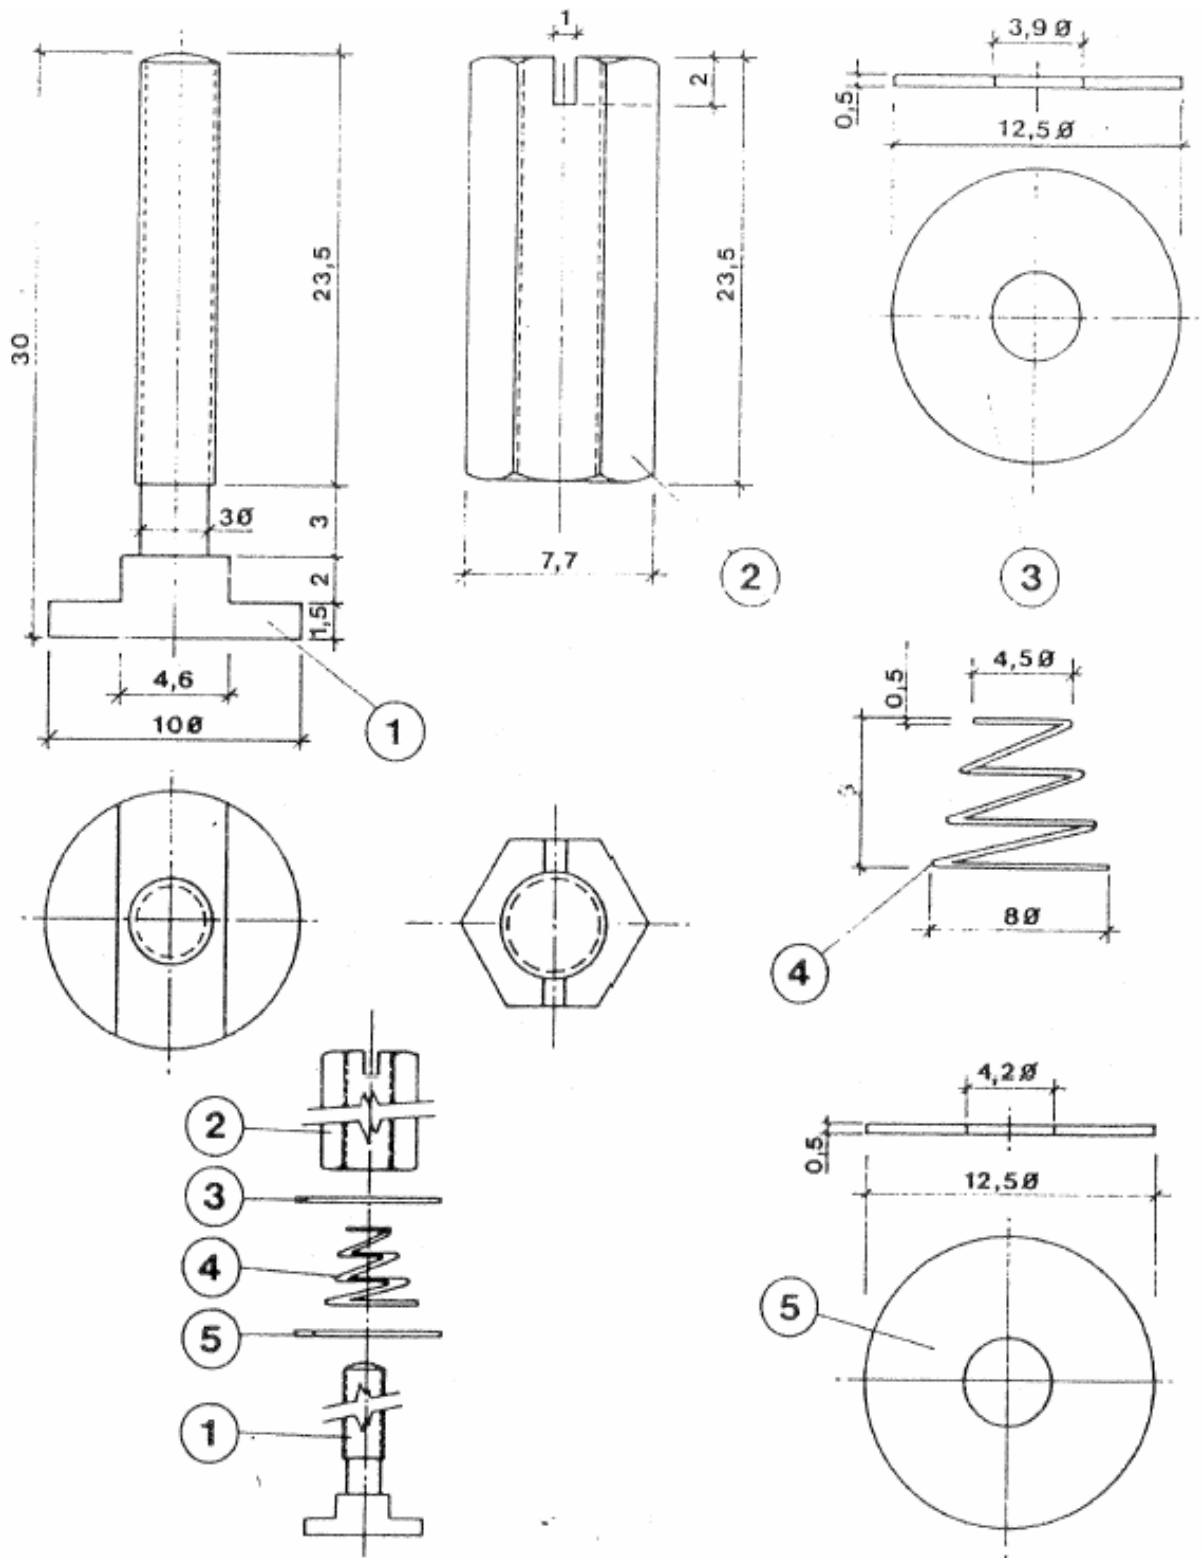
Panel de montaje de contadores. Dimensiones en mm
